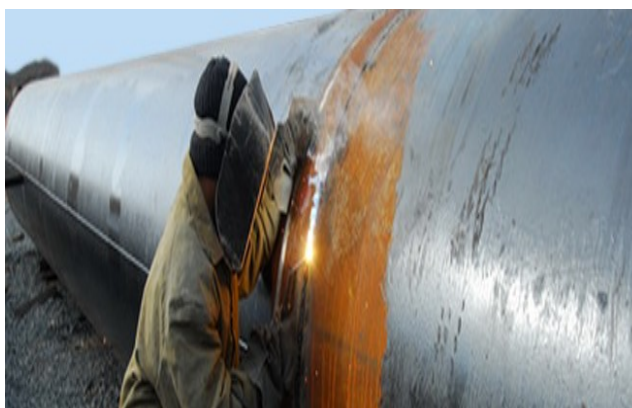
Дуговая сварка, труба 1420 мм
